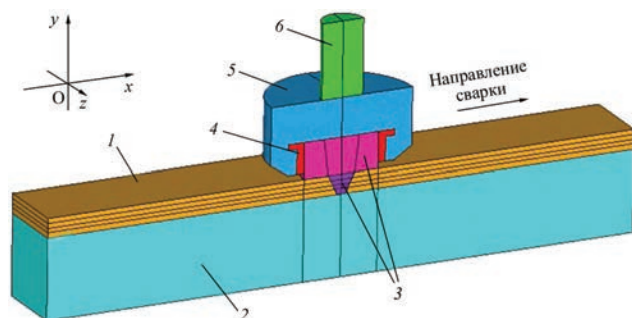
Схематическое изображение процесса СТП: 1, 2 — свариваемые детали; 3 — инструмент с буртиком; 4 — твердосплавная обойма; 5 — стальная державка; 6 — стальной вал привода
